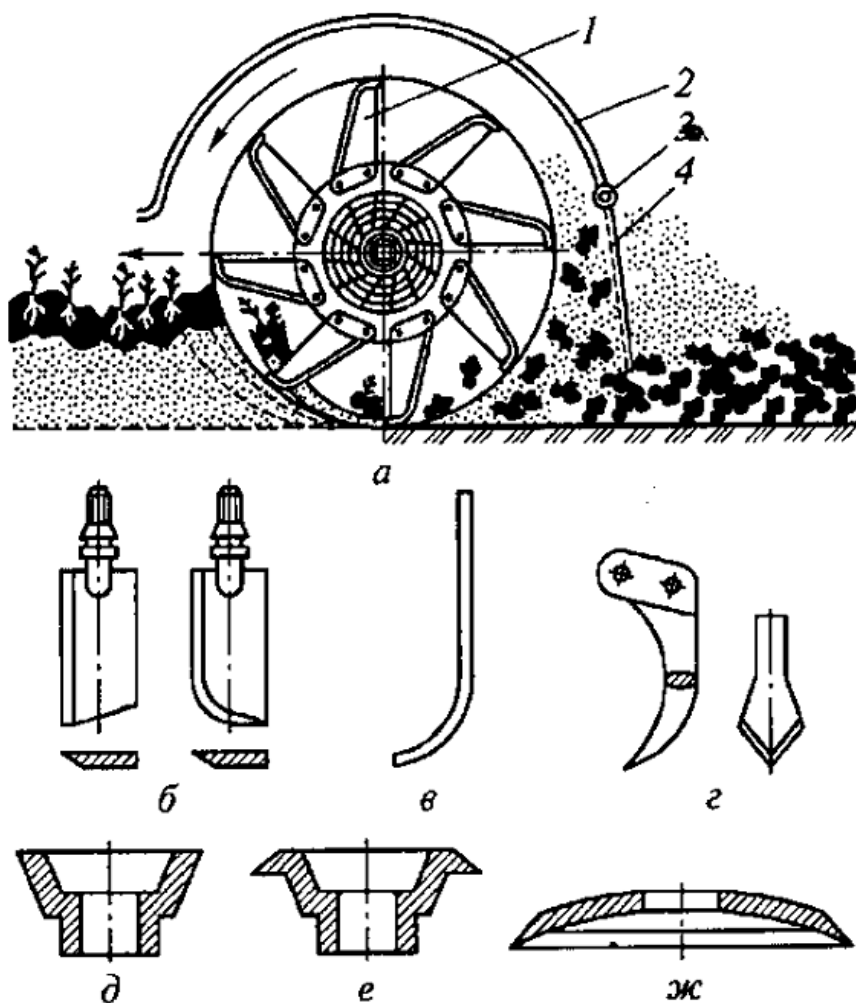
Рабочий орган фрезерных машин и его режущие элементы
